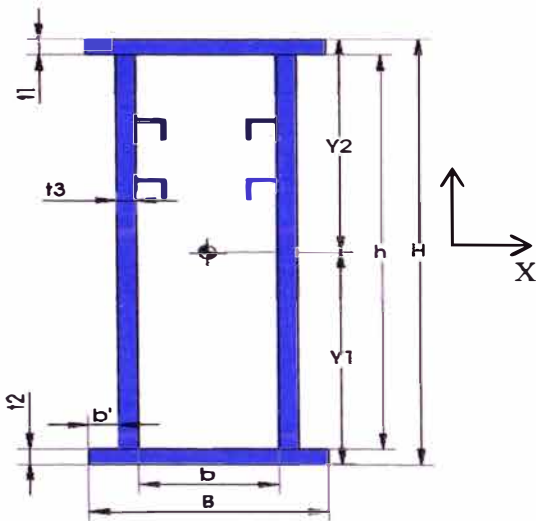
Perfil de viga cajón para FEM 2m
